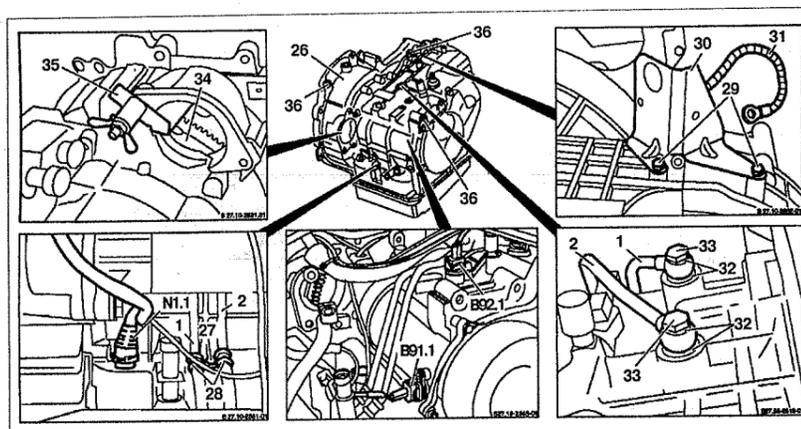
Снятие и установка АКПП (автомобили с двигателями 104.900):
